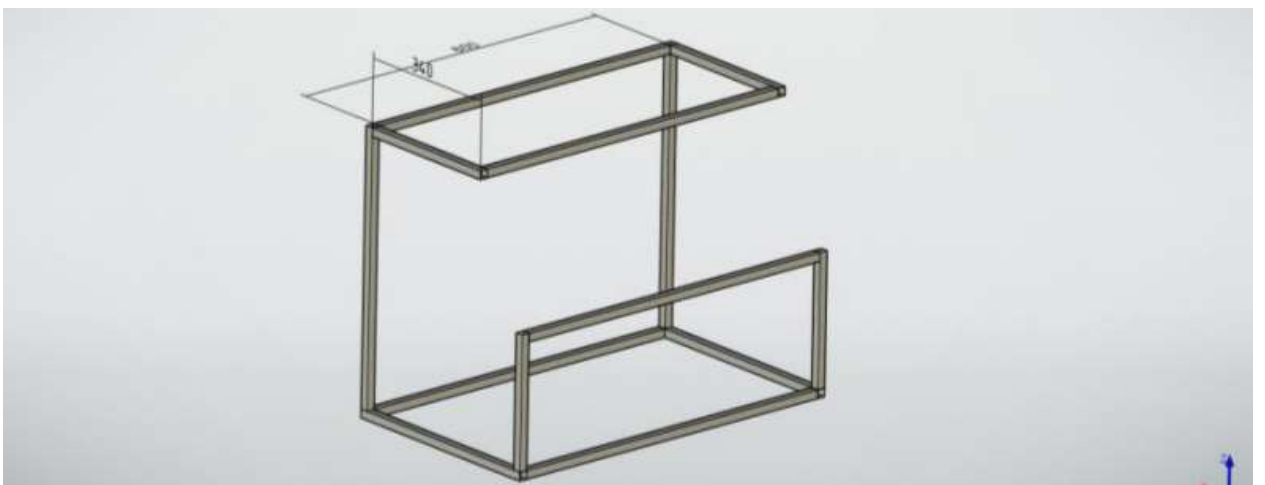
Узел №4 соединение с верхней частью корпуса
